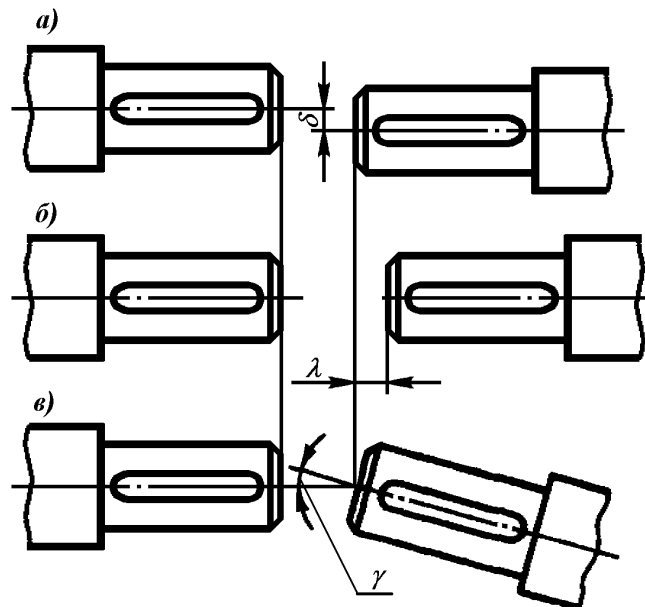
Виды возможного относительного смещения соединяемых валов: а) радиальное (поперечное); б) осевое (продольное); в) угловое.
